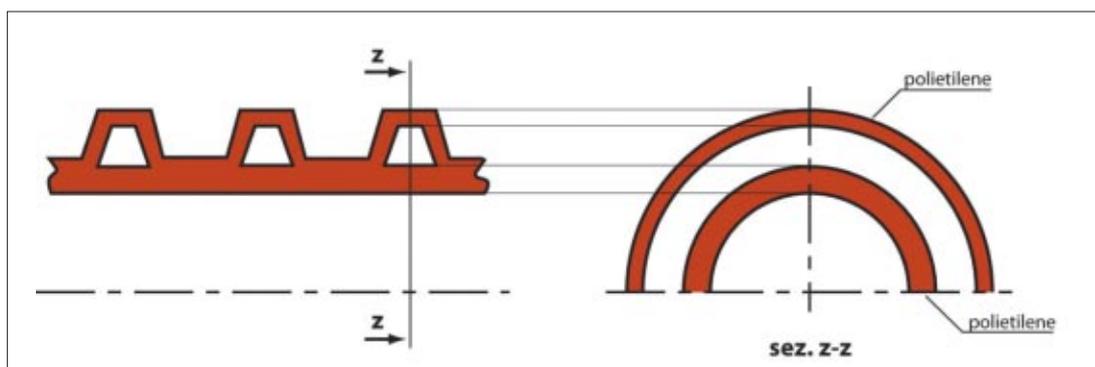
Sezione di una tubazione corrugata a doppia parete (tipo B secondo EN 13476-3: 2007)
